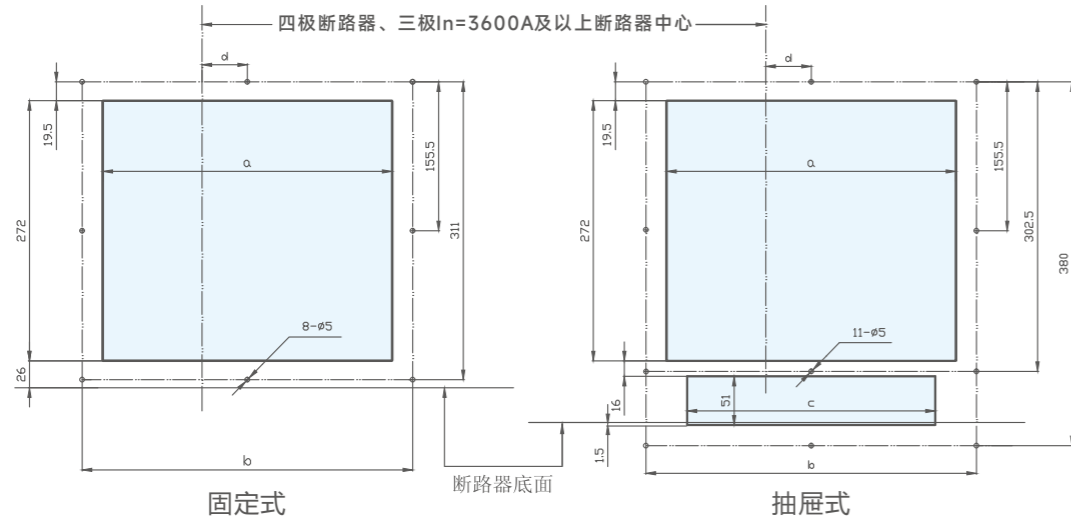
抽屉式断路器安装尺寸及外形尺寸 (FTW1-6300/3, In=6300A)
